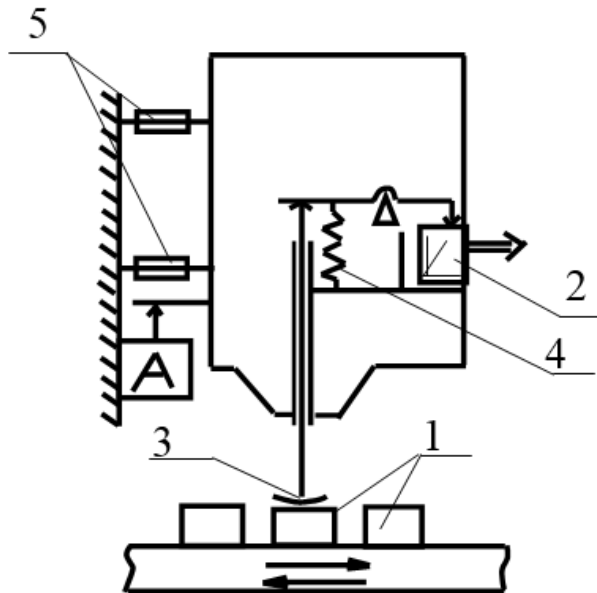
Вимірювальний пристрій для контролю висоти деталей:
